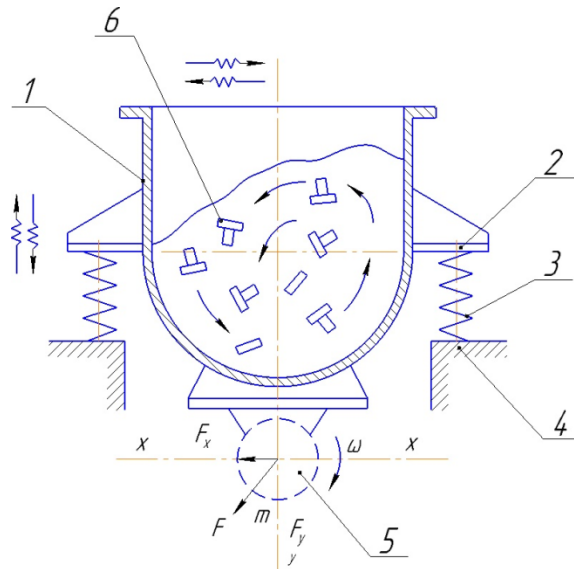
Принципова схема установки для очищення деталей вібраційним способом: 1 - робоча камера; 2 - платформа; 3 - пружини; 4 - основа; 5 - вібратор; 6 - деталь.
